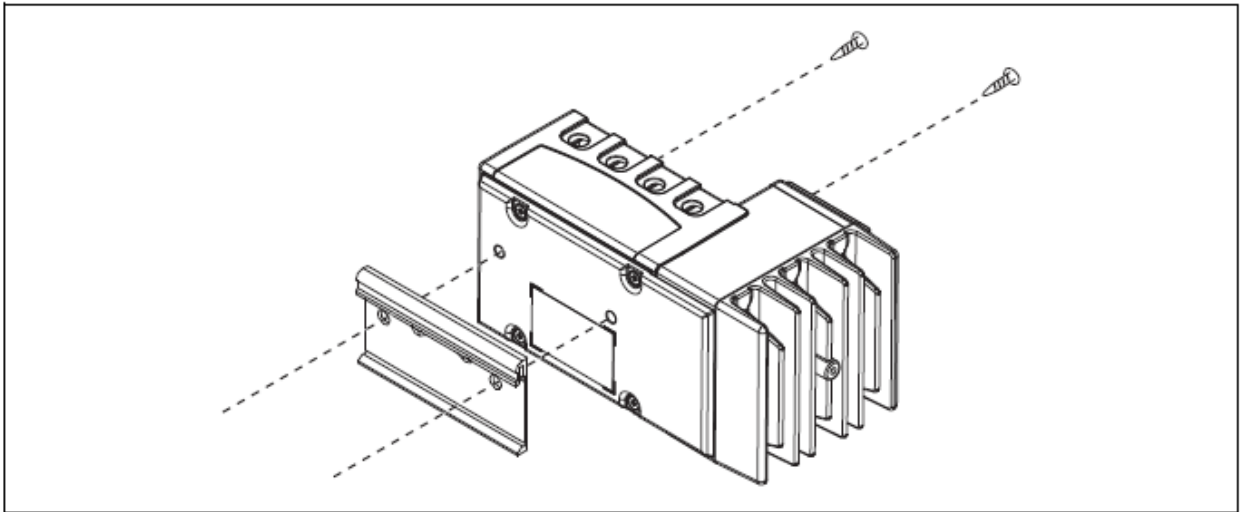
Установка фиксатора DIN-рейки на 4-слотовое шасси
